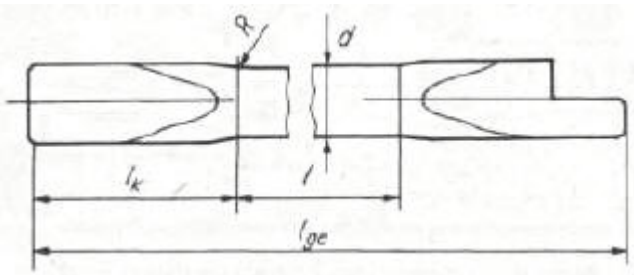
Hauptabmessungen einer Drehstabfeder
